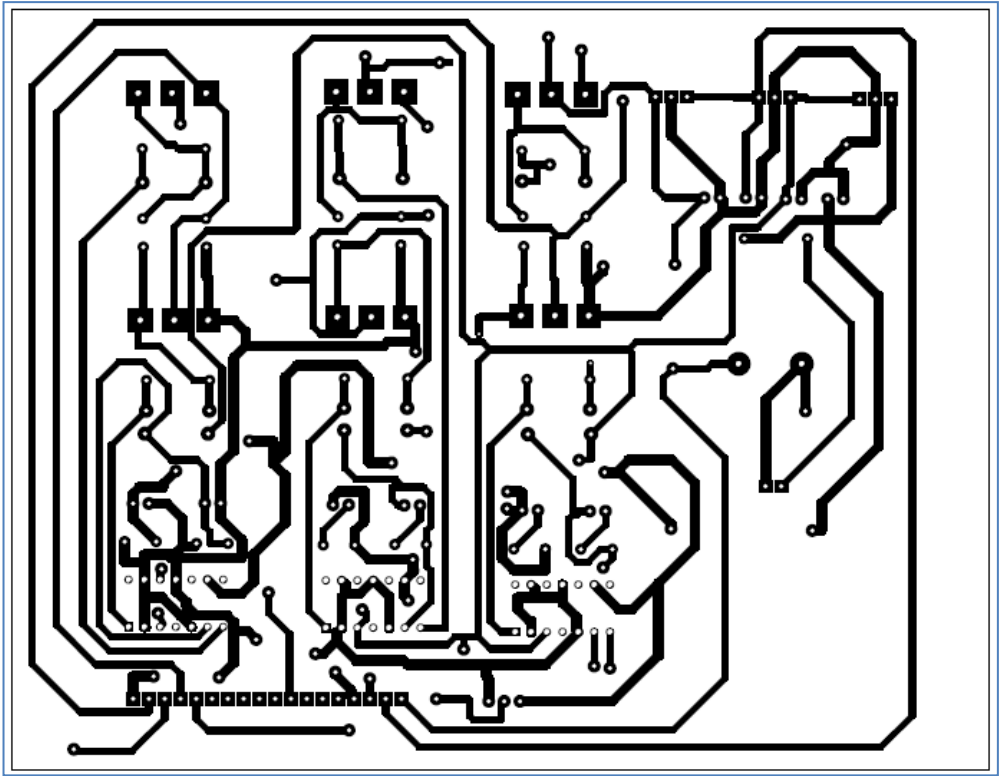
20 BLDC Motor Hız Kontrol Baskı Devre Görüntüsü
